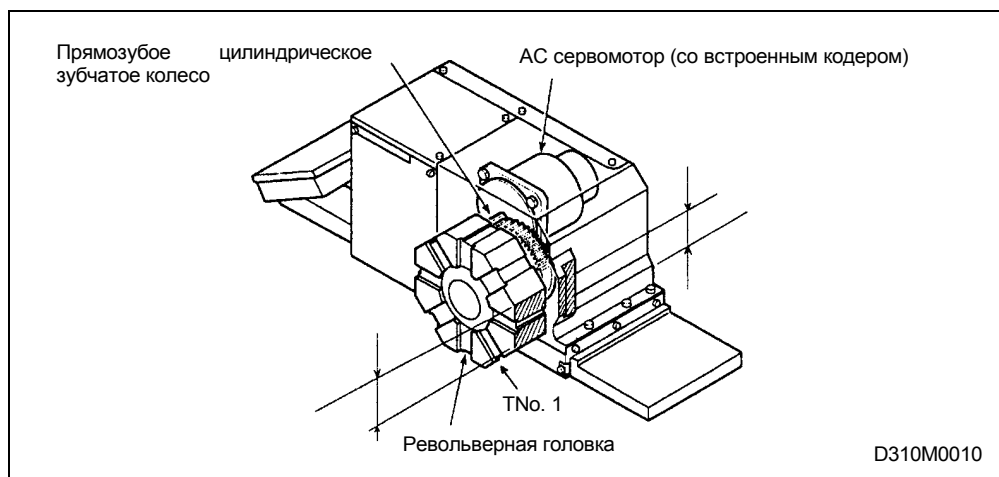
Установка исходной позиции для поворота револьверной головки (2/2)
